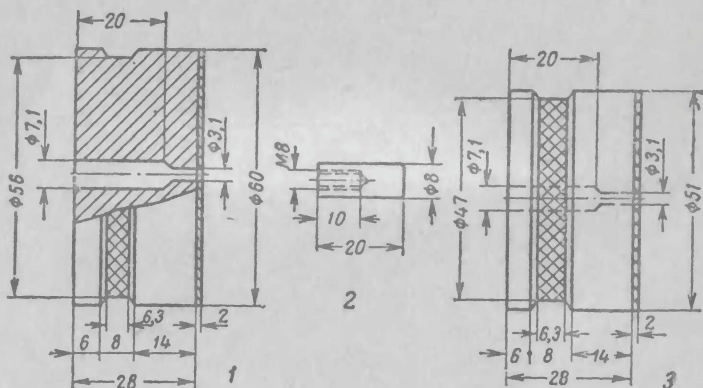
Конструкция ведущего вала магнитофонной приставки.
